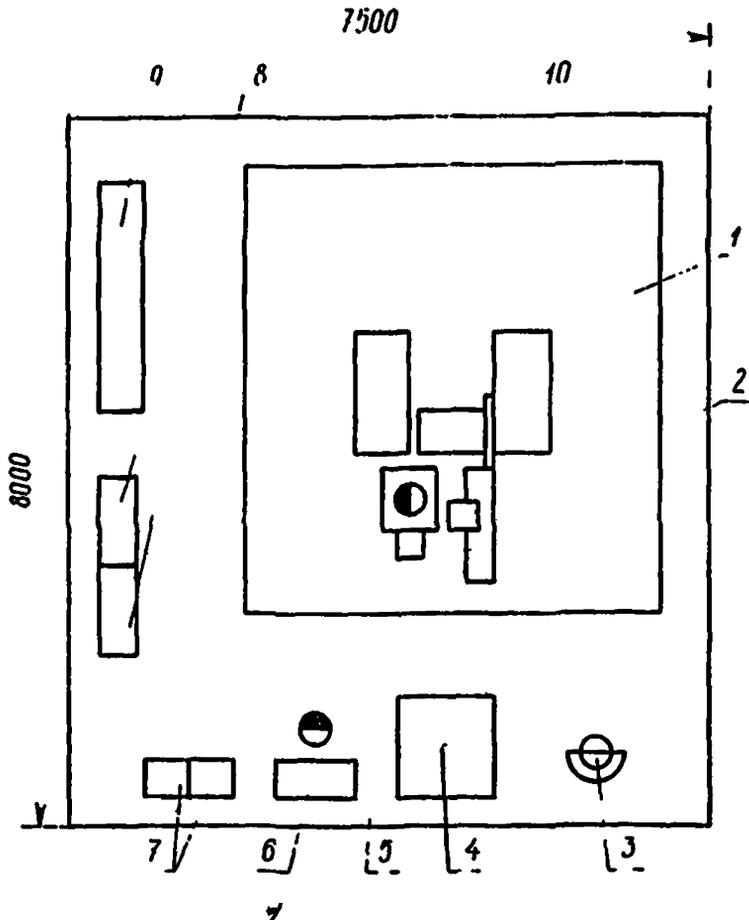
Схема организации рабочего места при электрошлаковой сварке кольцевых швов проволочными электродами:
